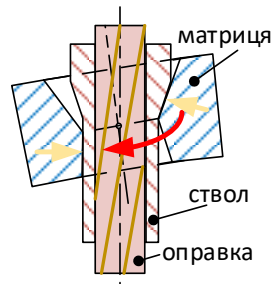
Схема обтиску ствольної заготовки редуціованням з обкочуванням
